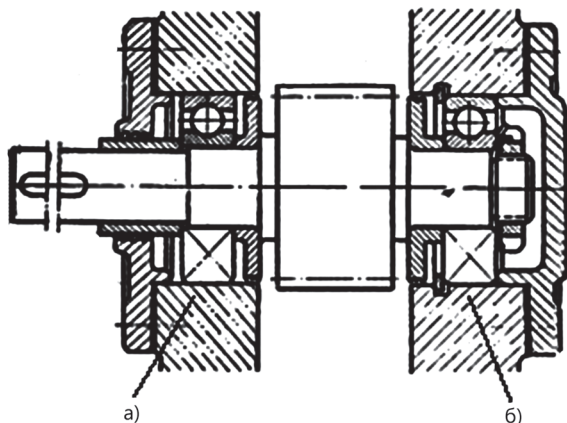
Подшипниковая сборочная единица, не извлекаемая из корпуса:
